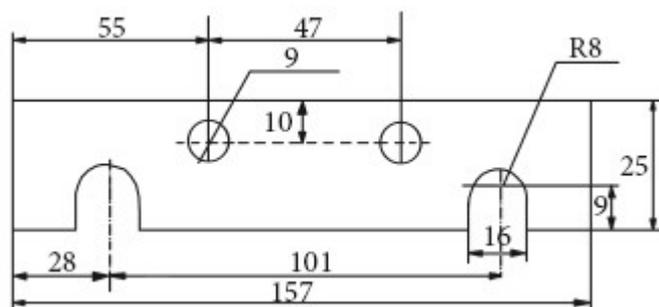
Приспособление для установки держателя заднего сальника коленчатого вала на автомобиле «Волга»
